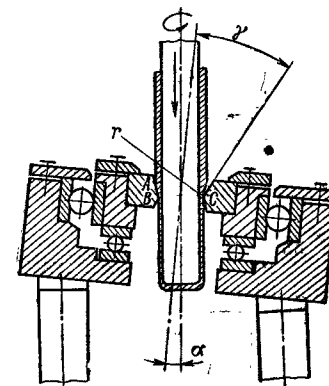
Способ утонения трубчатых деталей качающейся матрицей
